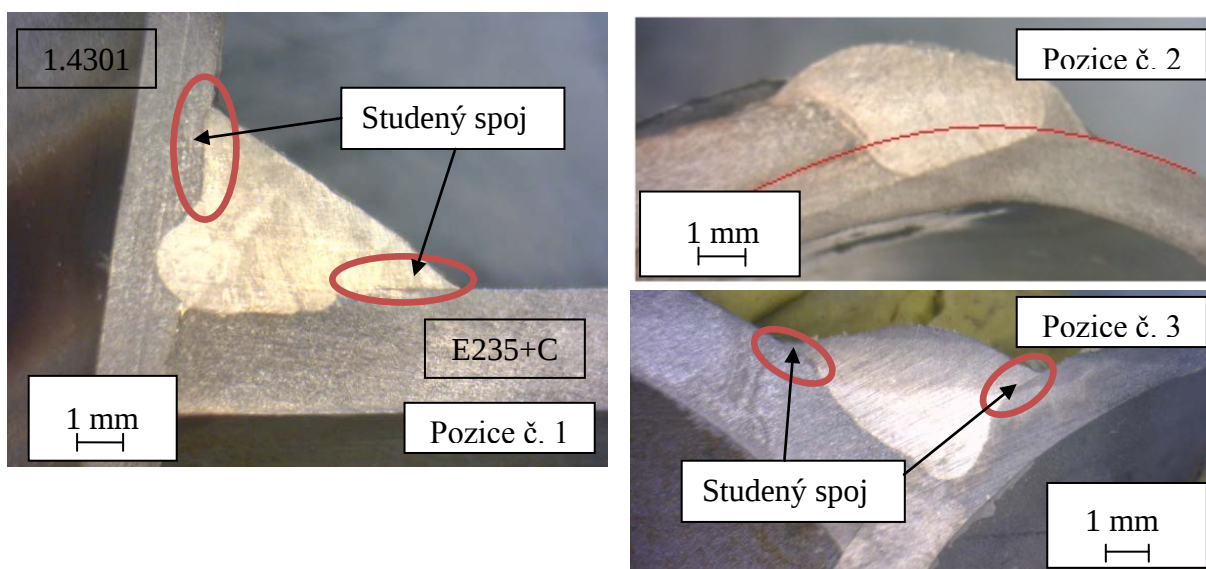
Makrostruktura svaru G4 vzorku č. 2
